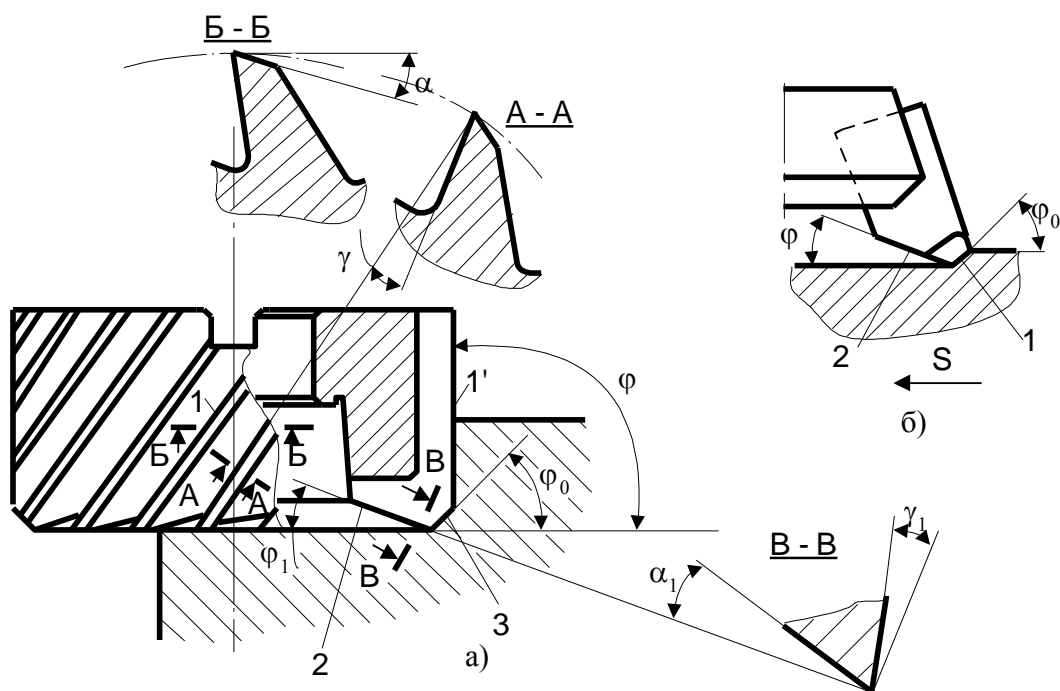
Геометрические параметры острозаточенных фрез с цилиндрической (а) и конической (б) главными режущими кромками
